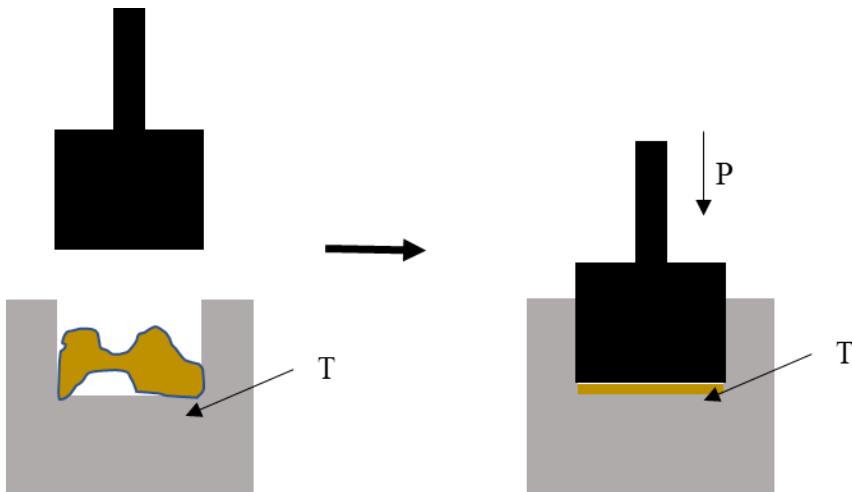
Esquema del método de procesado mediante moldeo por compresión.
